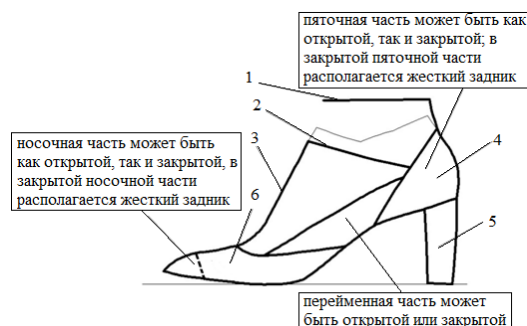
Схема расположения деталей из меха в конструкции туфель закрытого, открытого типа и ремешковой обуви:
